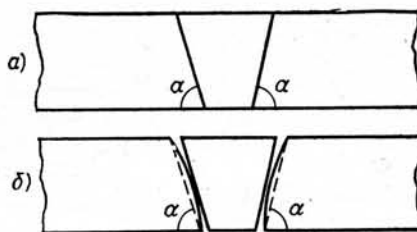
Распорный стык, заполняемый клиновым вкладышем: а — при плоской поверхности; б — при цилиндрической
